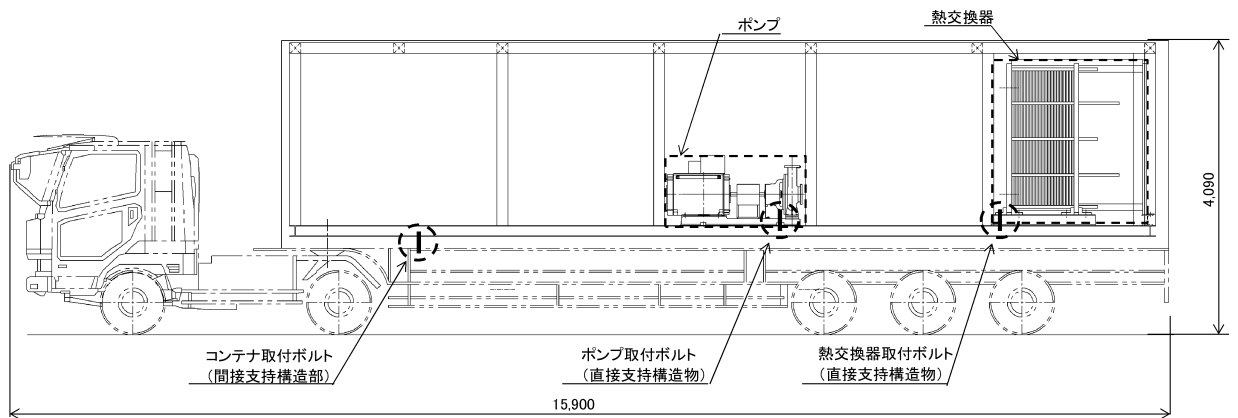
移動式代替熱交換設備の構造図 (単位: mm)
